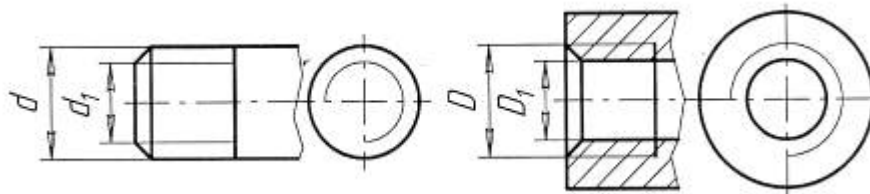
Изображение наружной и внутренней резьбы на чертежах
